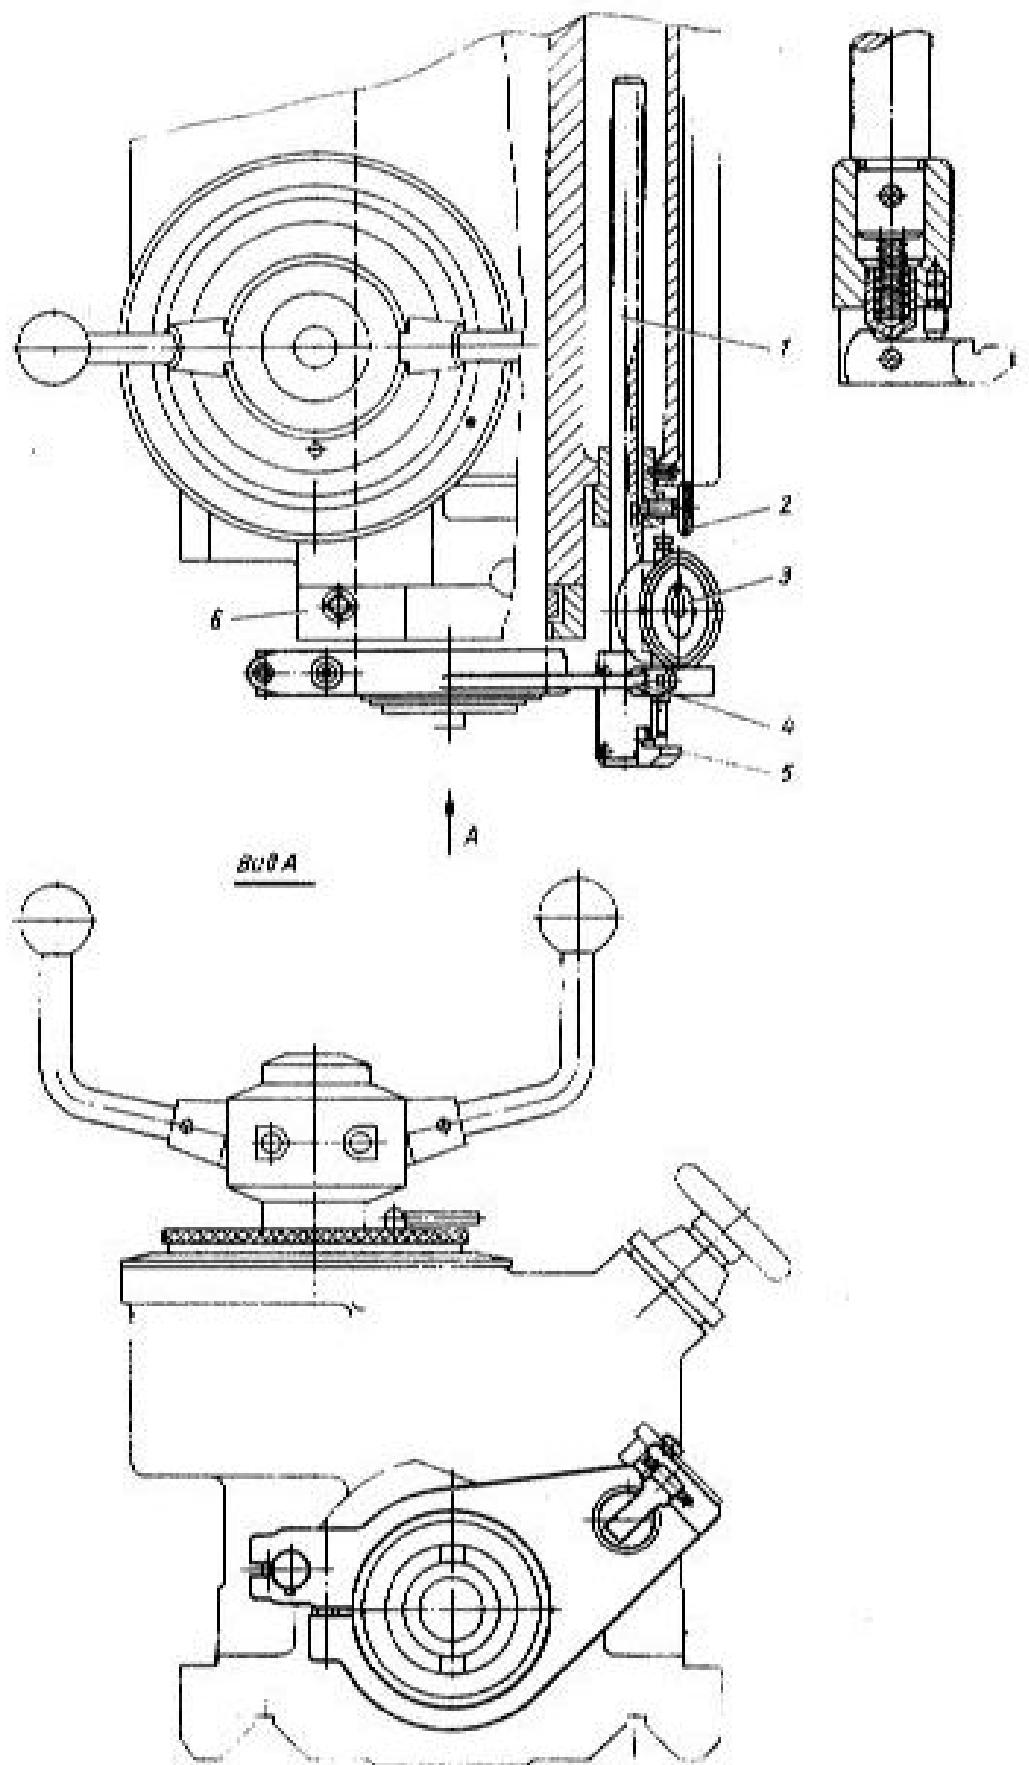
Приспособление для измерения эксцентриситета колеса судна винздория
